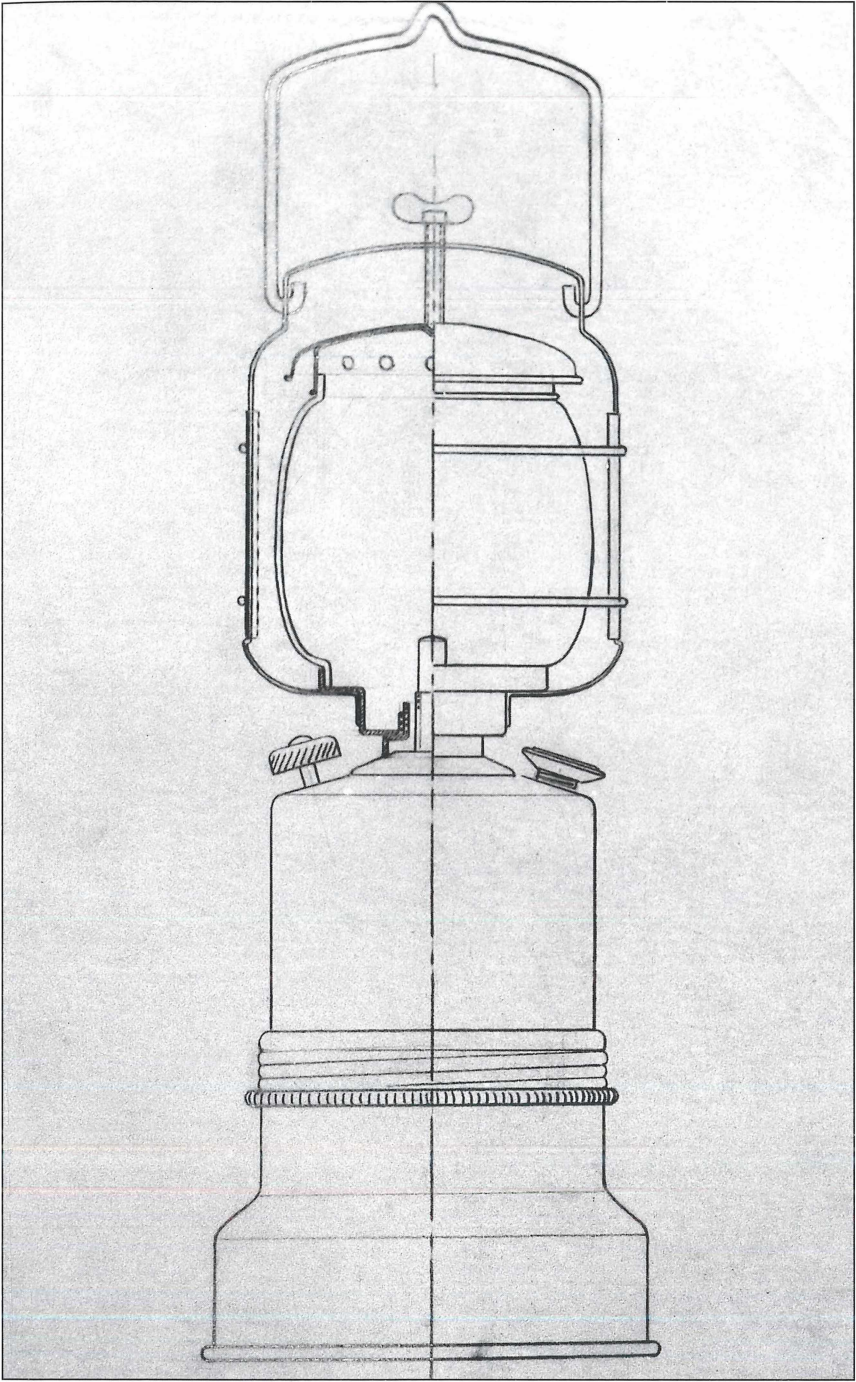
Konstruktionszeichnung einer Sturmlaterne mit Schraub-Ring-Verschluss
